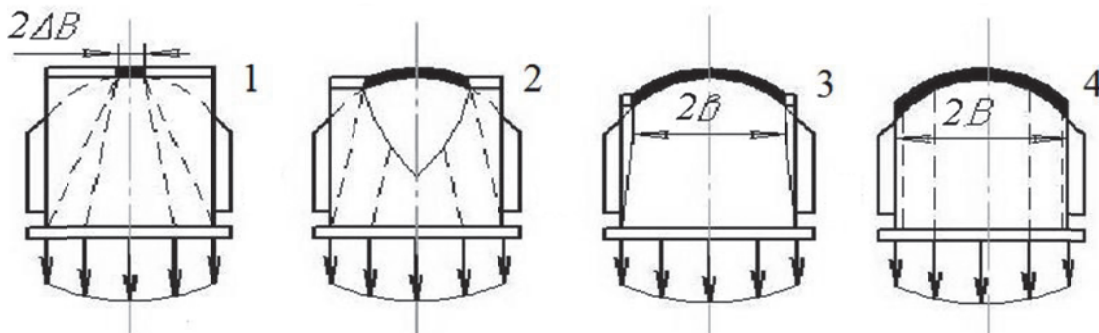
Предварительная обтяжка оболочки двояковыпуклой формы после полного оборачивания обтяжного пуансона листовой заготовкой на угол α_k
